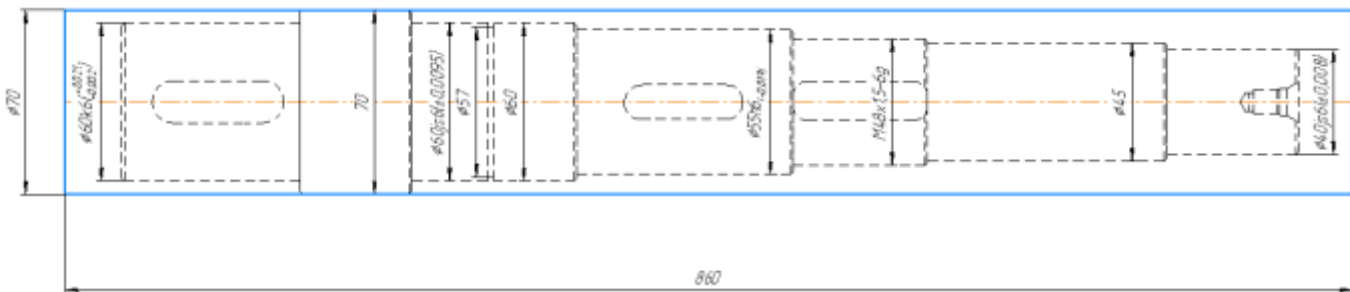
Ескіз заготовки з прокату гарячекатаного круглого звичайної точності.
